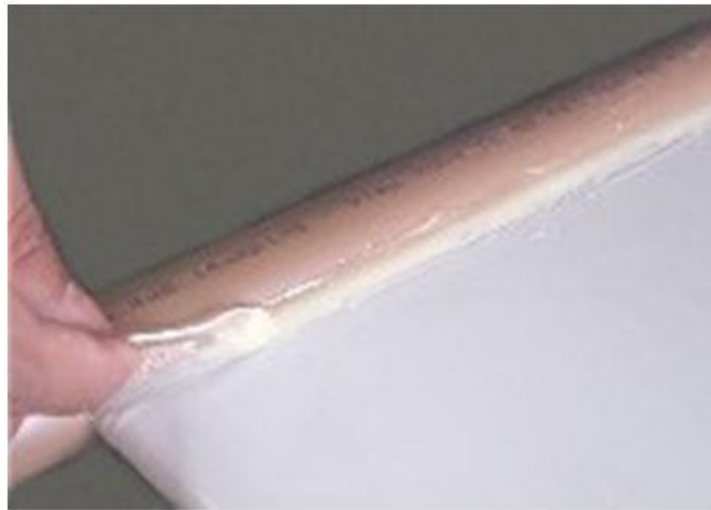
Soldando o tubo 32 mm e a placa de PVC modular.
